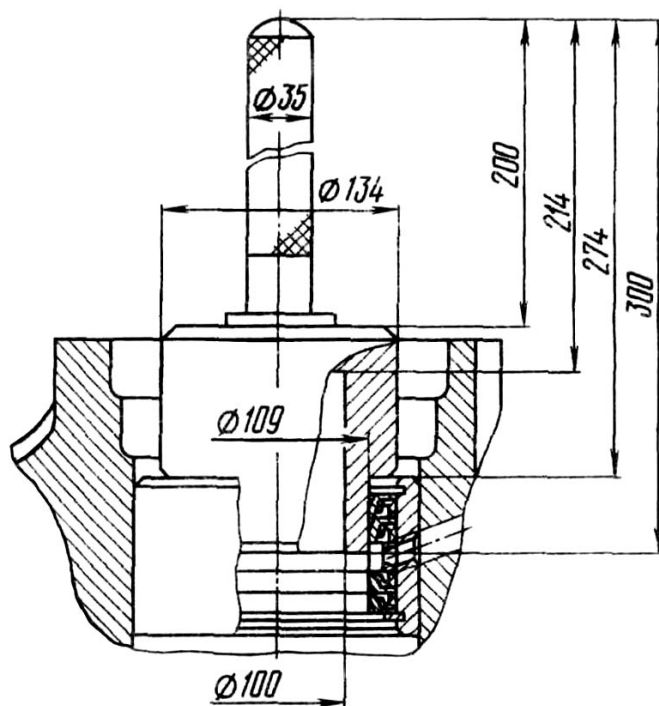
Запрессовка оправкой комплекта деталей уплотнительного устройства
